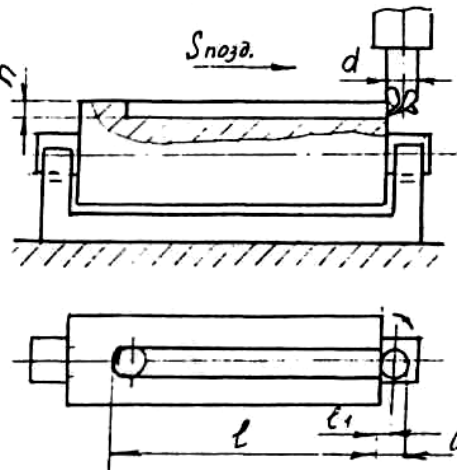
Схема фрезерування канавки відкритої з одного боку
